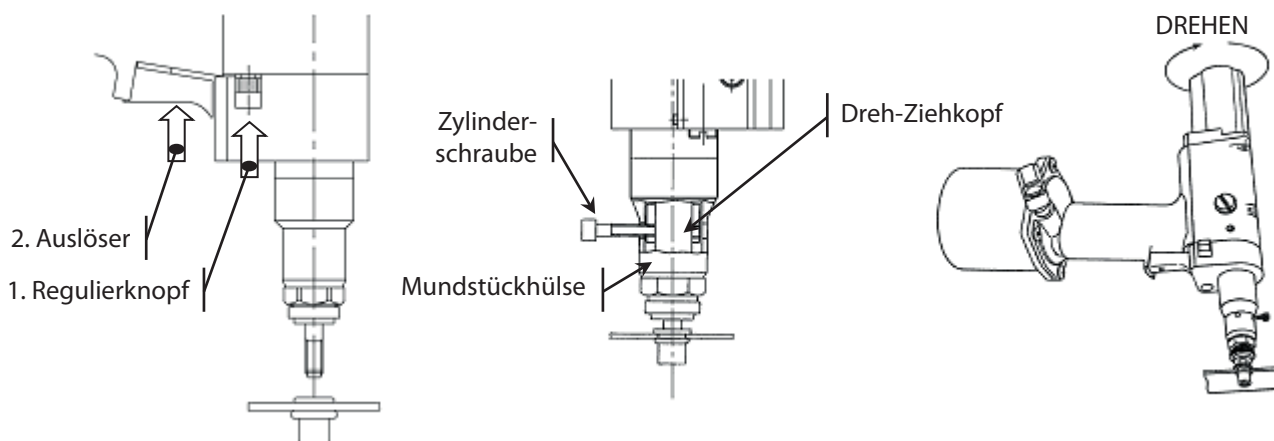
Lösen des Werkzeugs von der Blindnietmutter
